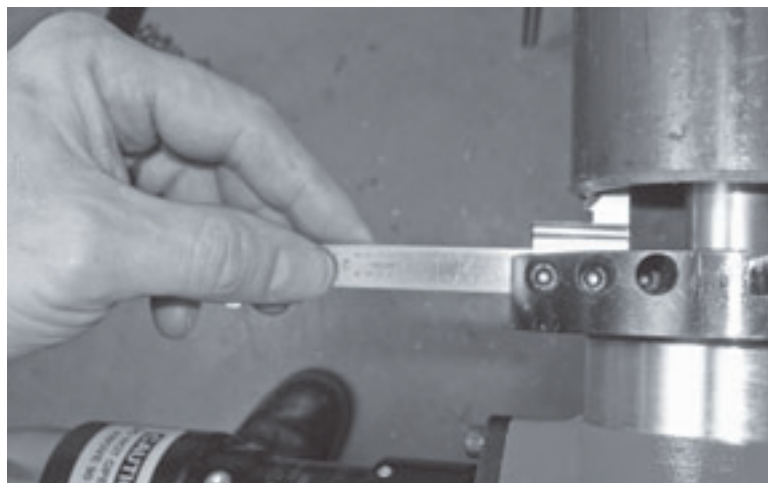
Verwenden Sie einen Messschieber, um das Innenbearbeitungswerkzeug korrekt zu positionieren.
